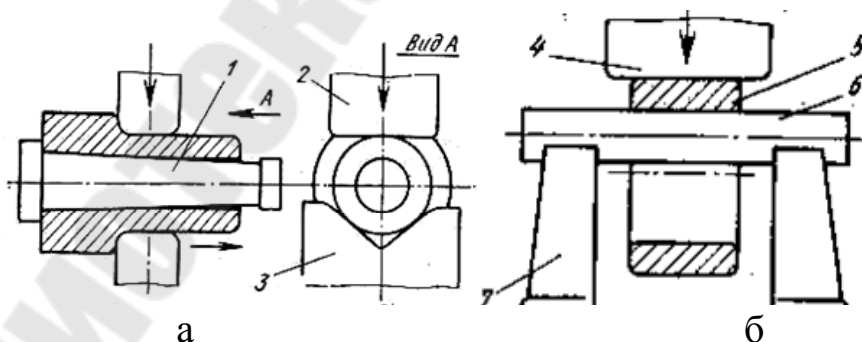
Схема протяжки (а) и раскатки (б) заготовки на оправке
